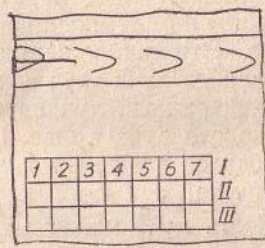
Схема контроля (а) и ультразвукограмма (б) стыкового сварного шва с частичным непроваром; толщина металла 20 мм.
